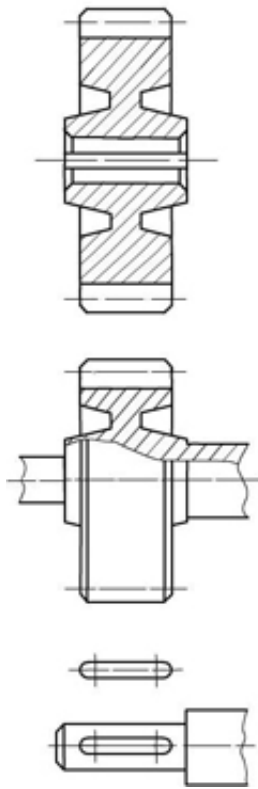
Шлицевый вал в отверстии зубчатого колеса, шестерни отдельно
